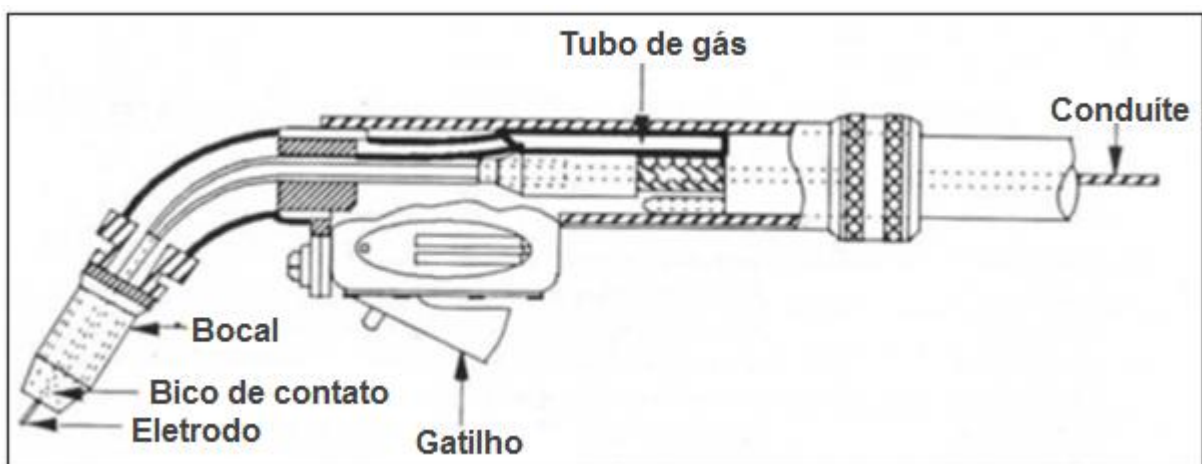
Tocha de soldagem MIG/MAG [Figueiredo, 2005].
